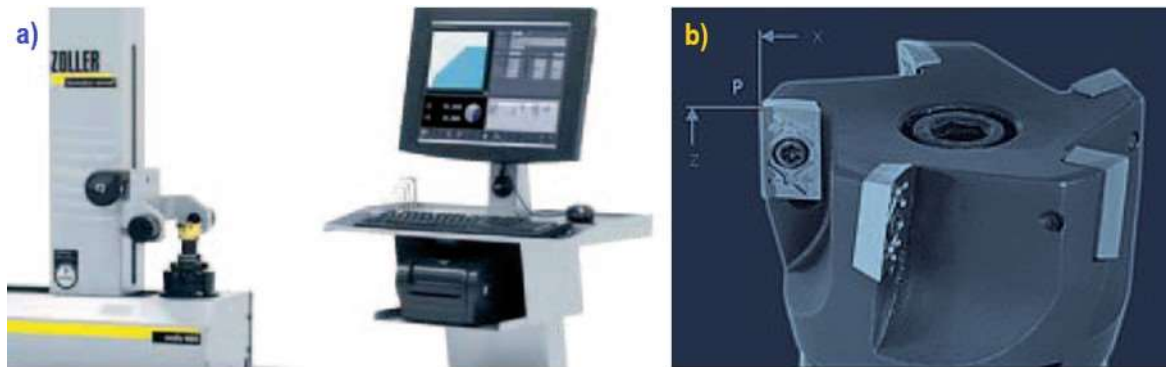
Medición del inserto: a) máquina de medición de herramienta de corte y b) medición de un inserto de fresado. [85], [86]
